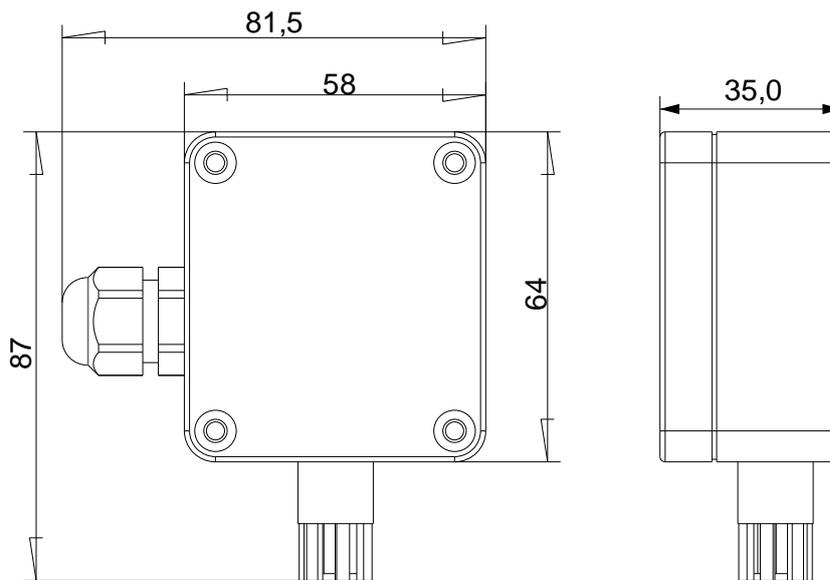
Габаритные размеры датчика JLS30HW
